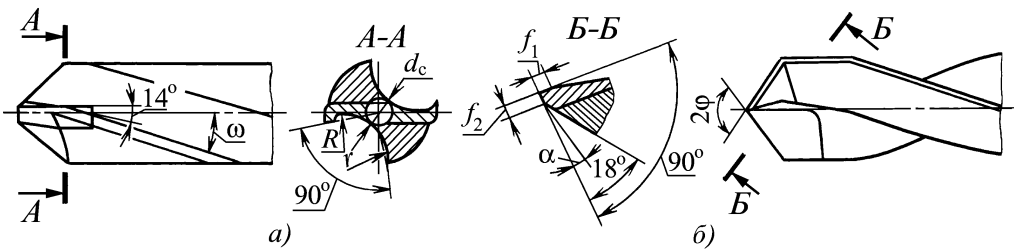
Сверло, оснащенное пластинами из твердого сплава:
